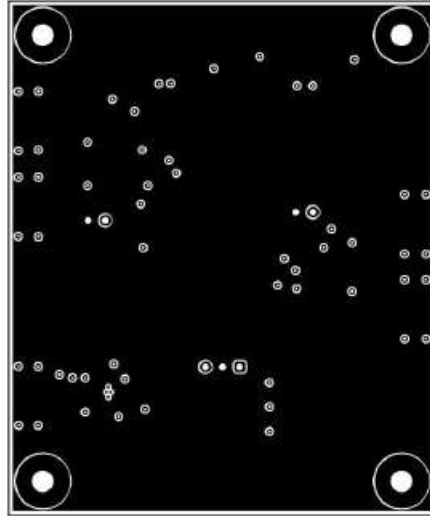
LMK6 EVM の PCB レイアウト例 - GND レイヤ 2
